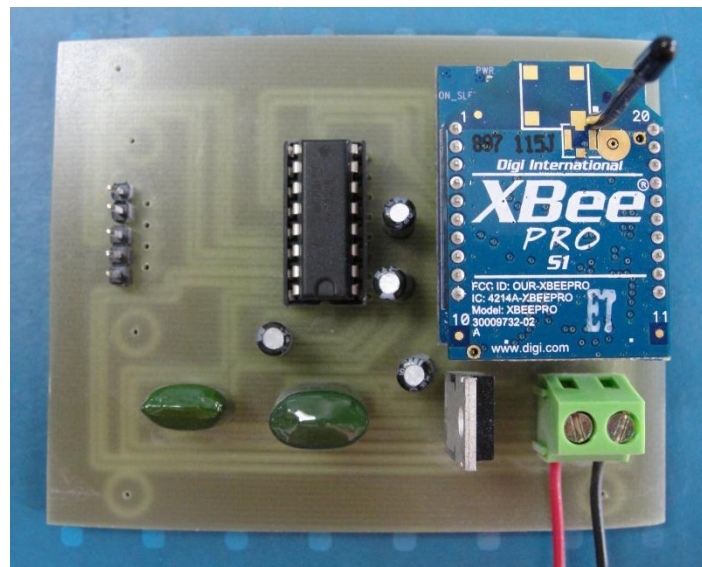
PCB en placa de sensores ultrasónicos y acelerómetro
